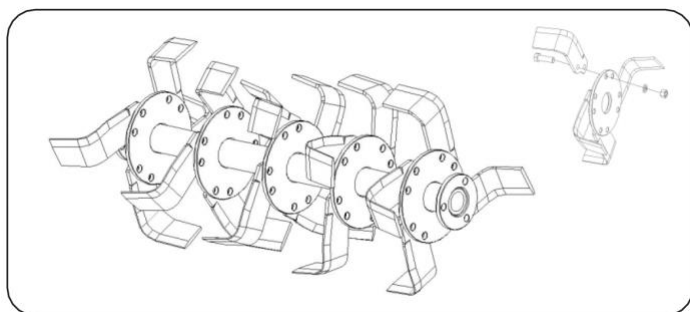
Схема установки ножей на ротор и направление монтажа крепежа
